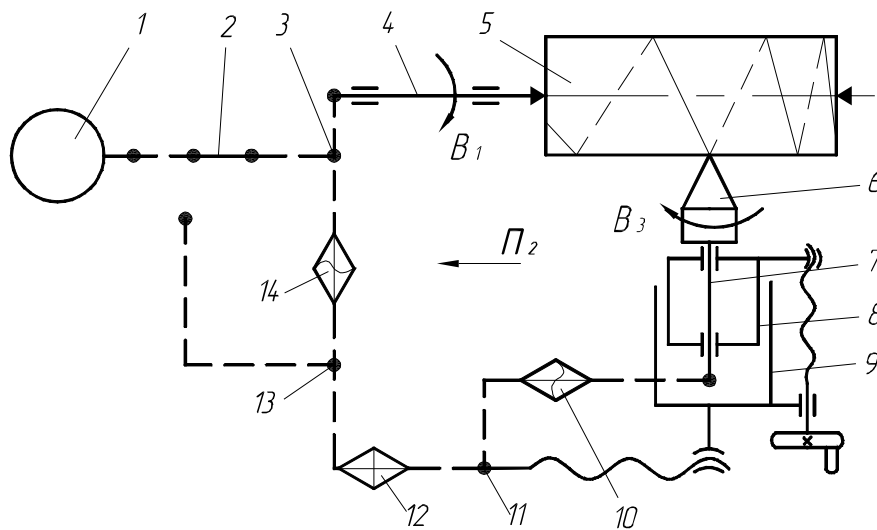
Структурная схема станка для обработки винтовых поверхностей переменного шага с управляемым положением звена соединения связей
